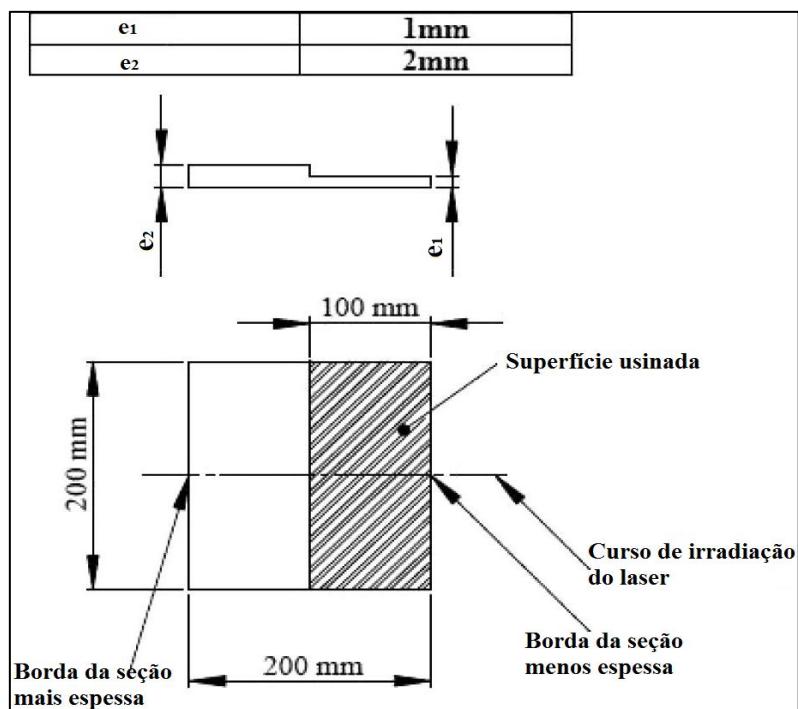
Exemplo de Tailor Machined Blank
